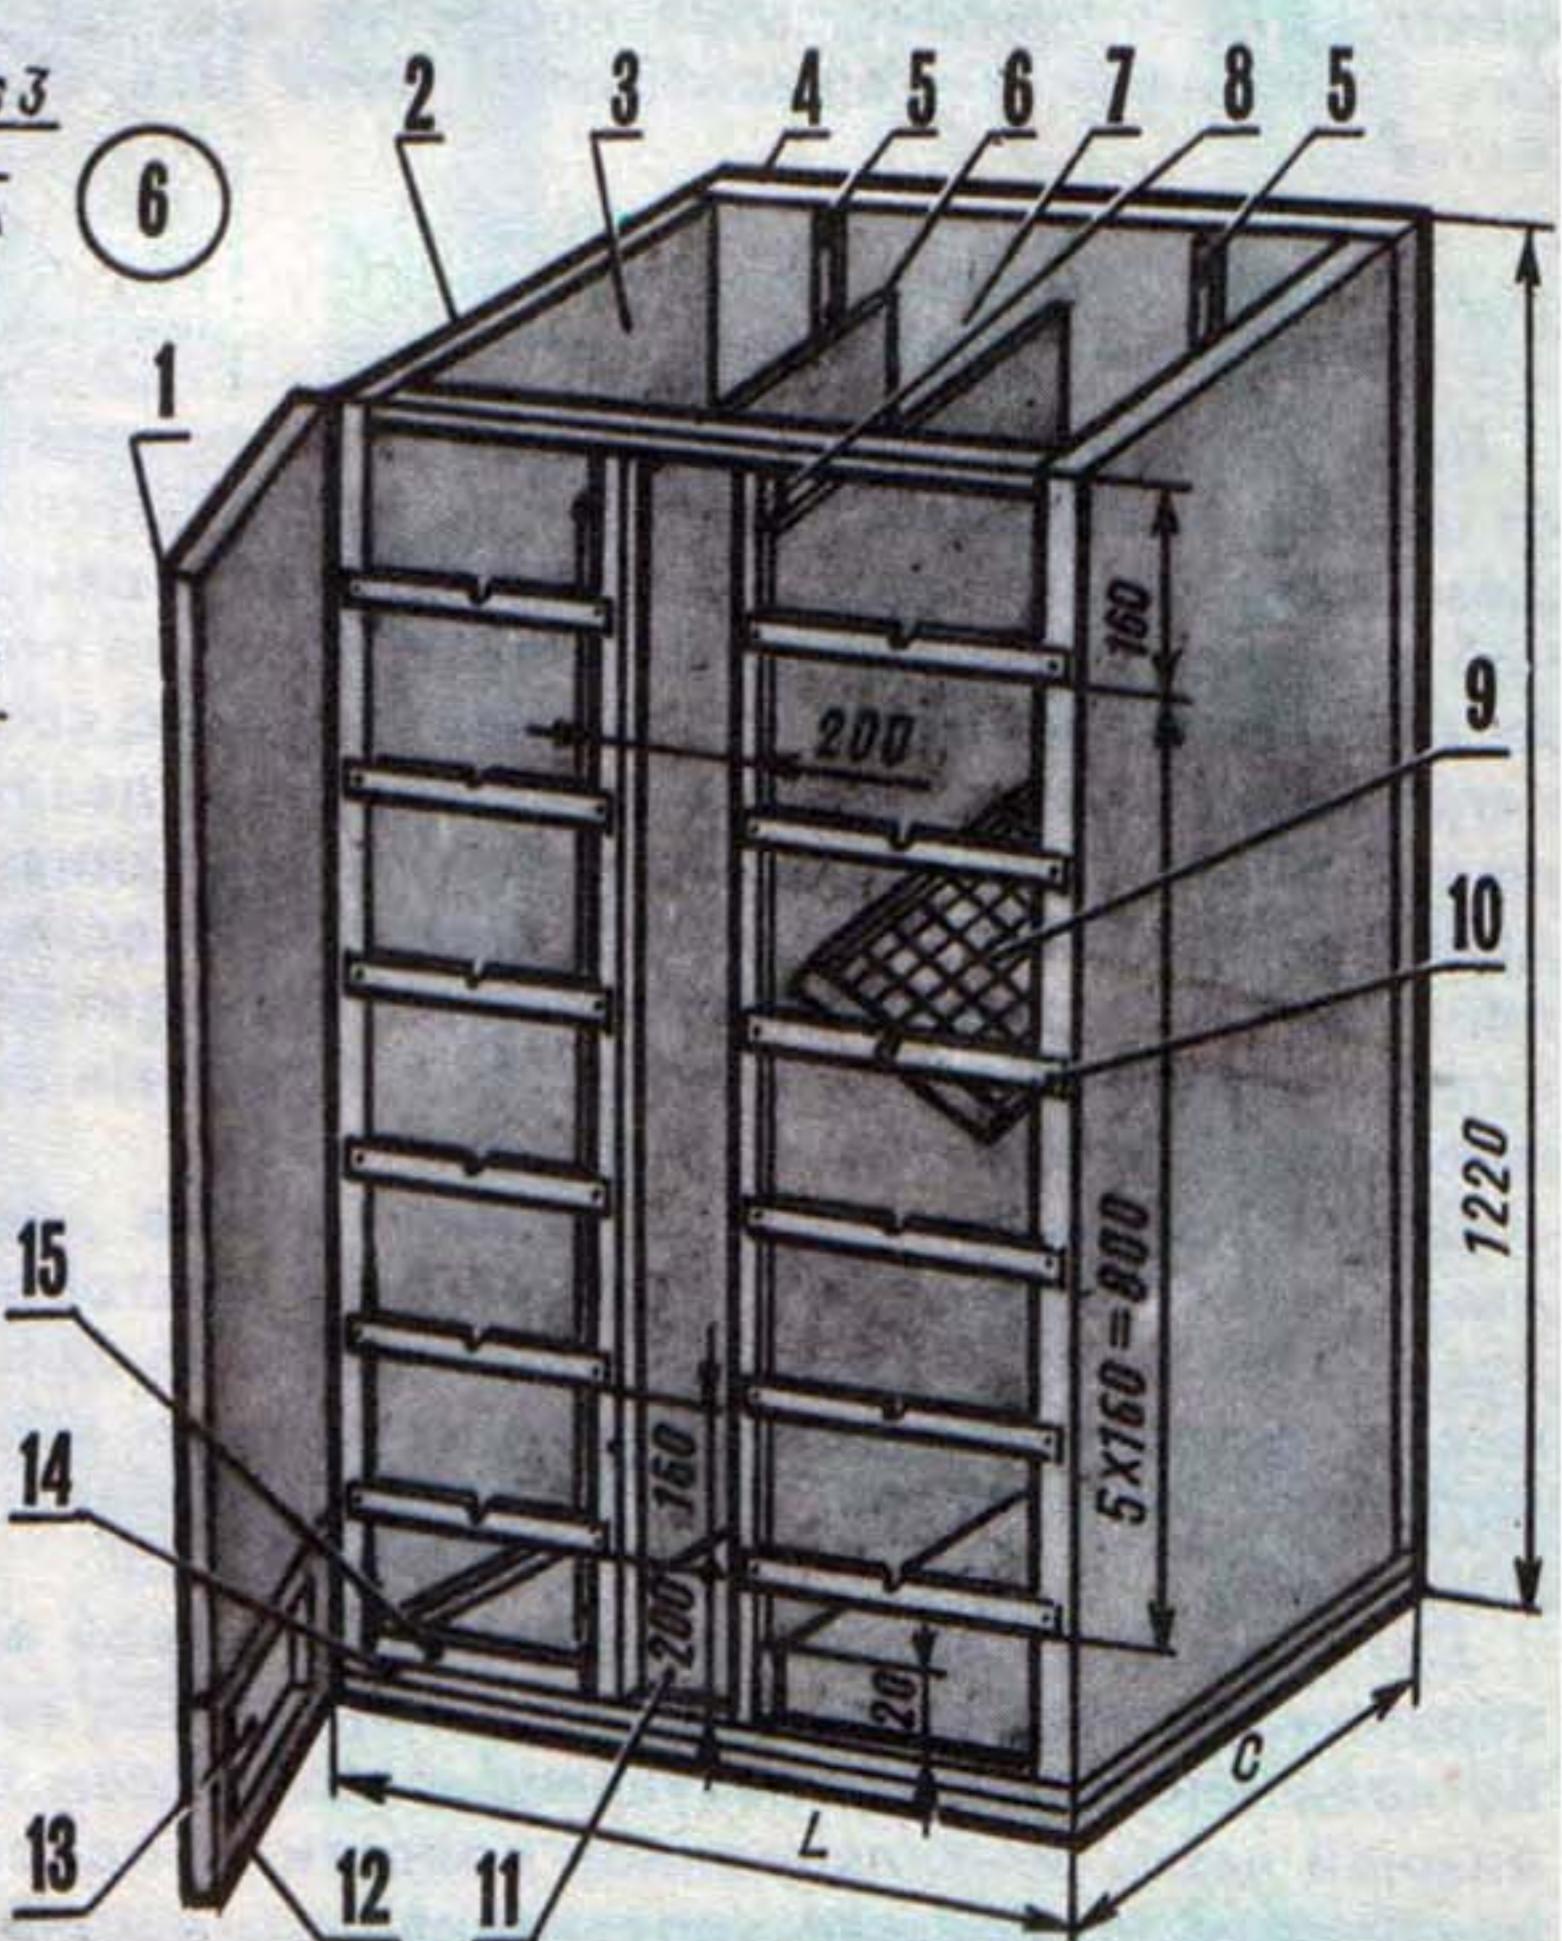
Двухкамерный шестиярусный инкубатор:
